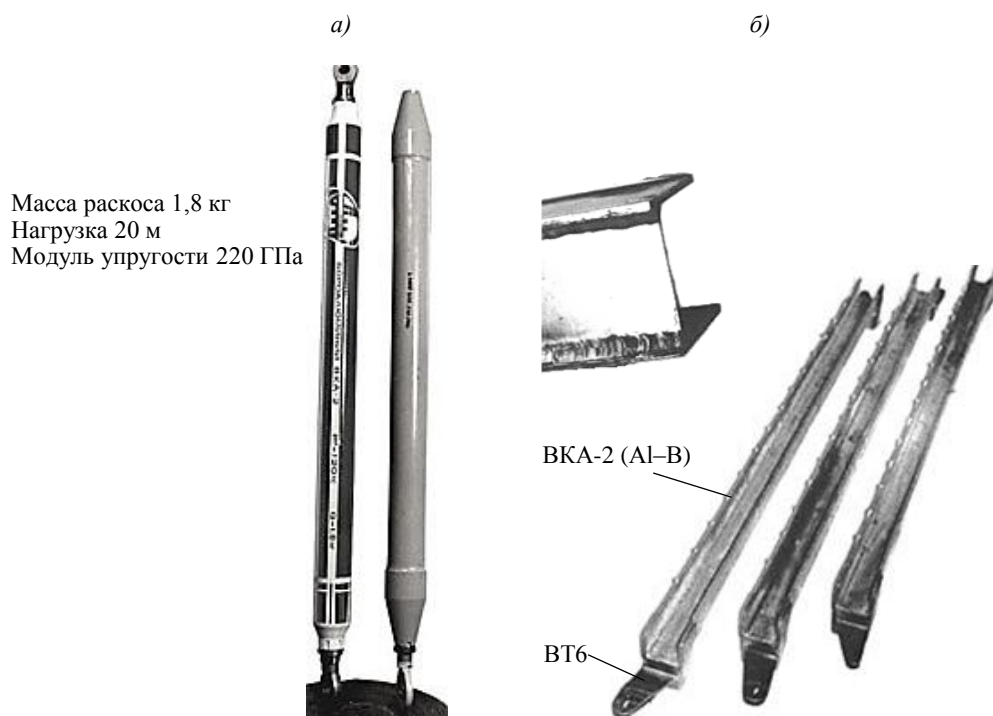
Трубчатые раскосы в конструкции шасси самолета «Руслан» (а) и сварные балки самолета Ан-70 (б) [26]
